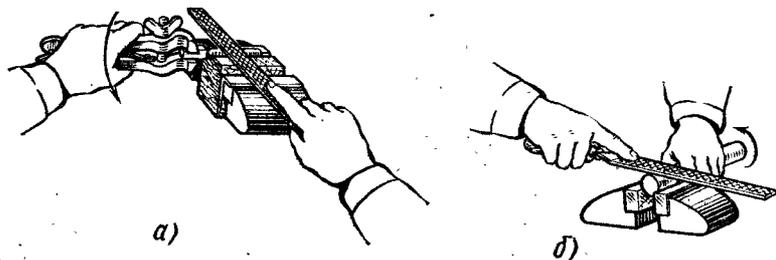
Приемы опиливания цилиндрической поверхности: а — на деревянном бруске; б — на губках тисков
